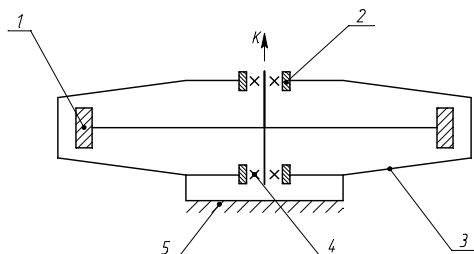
Электродвигатель-маховик: 1 – маховик; 2 – втулка; 3 – корпус; 4 – шарикоподшипник; 5 – установочная поверхность
